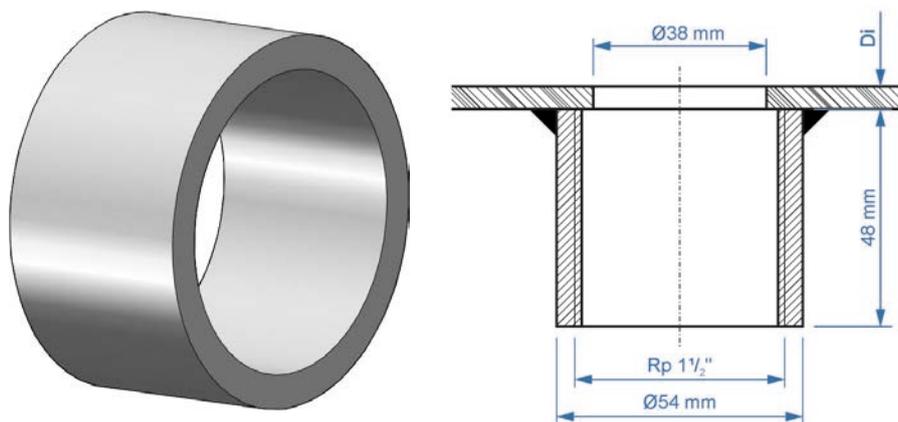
Ansicht und Maße für Anschweißstutzen gerade
